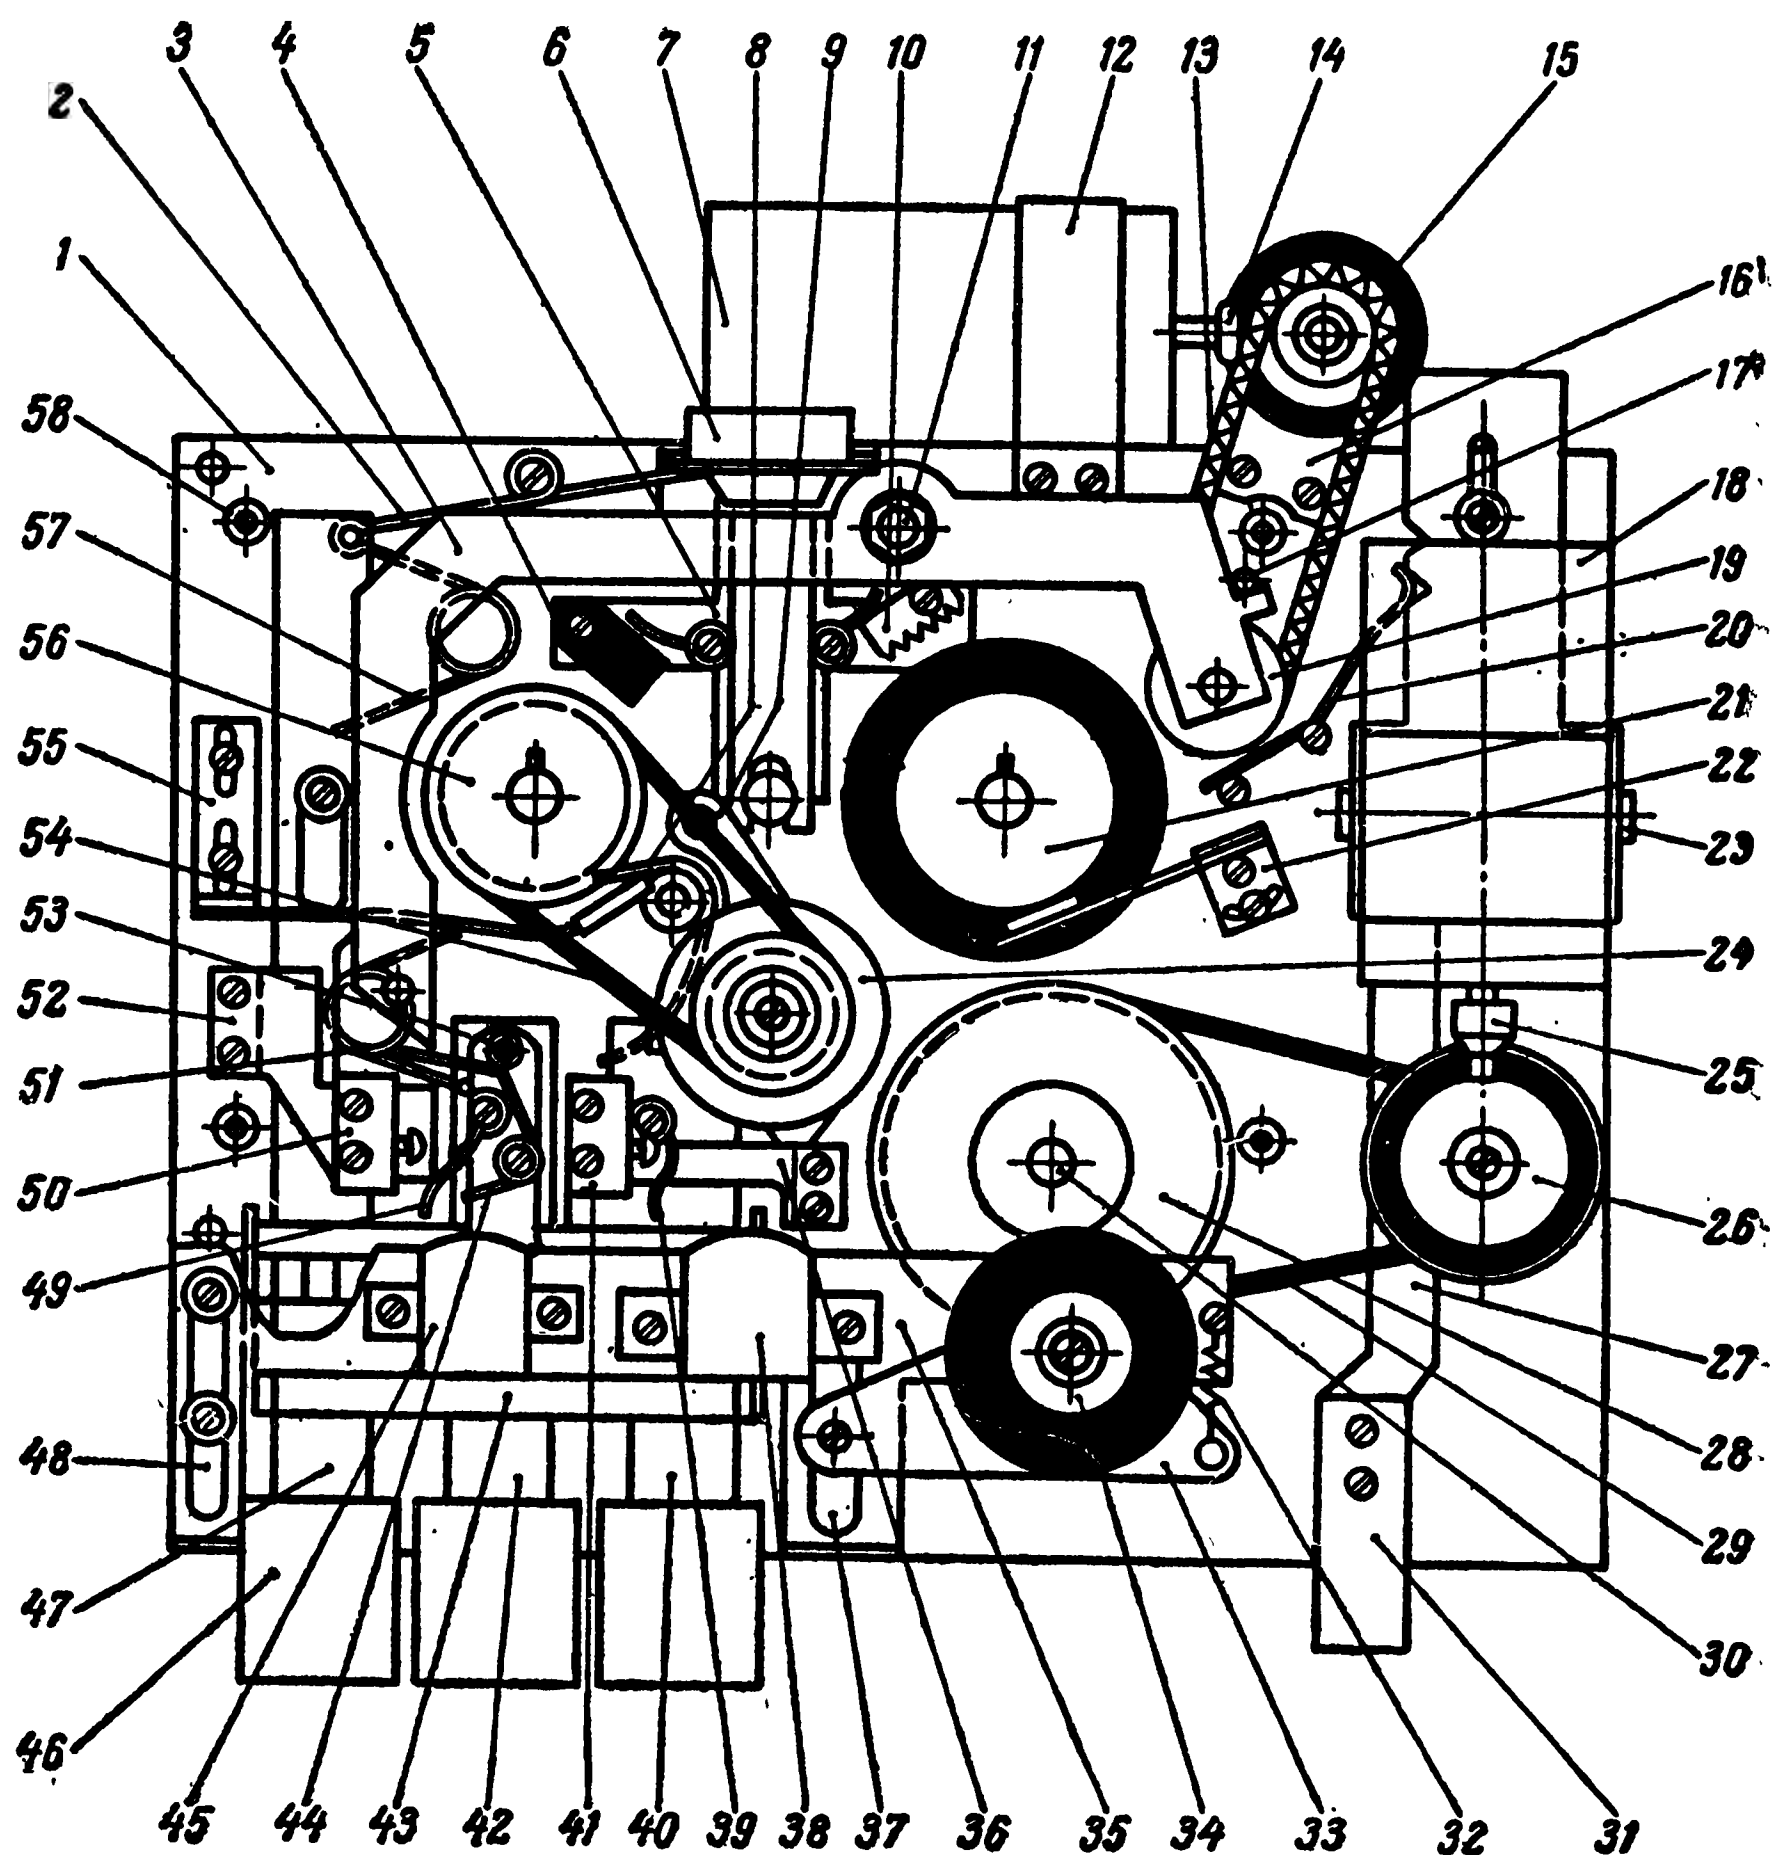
Сборочный чертеж лентопротяжного механизма.
